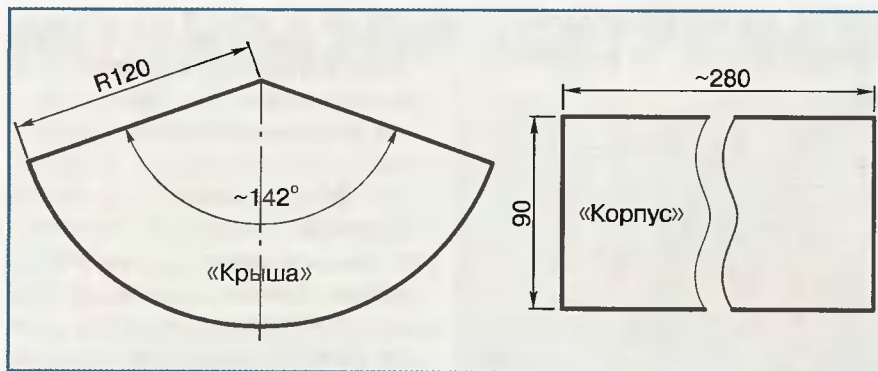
«Выкройки» шаблонов для изготовления деталей керамического корпуса аэроионизатора.
